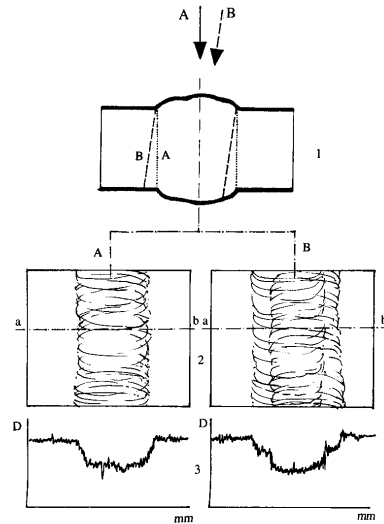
Efecto de superposición oblicua de las imágenes de los cordones de una soldadura en "X" simétrica.
